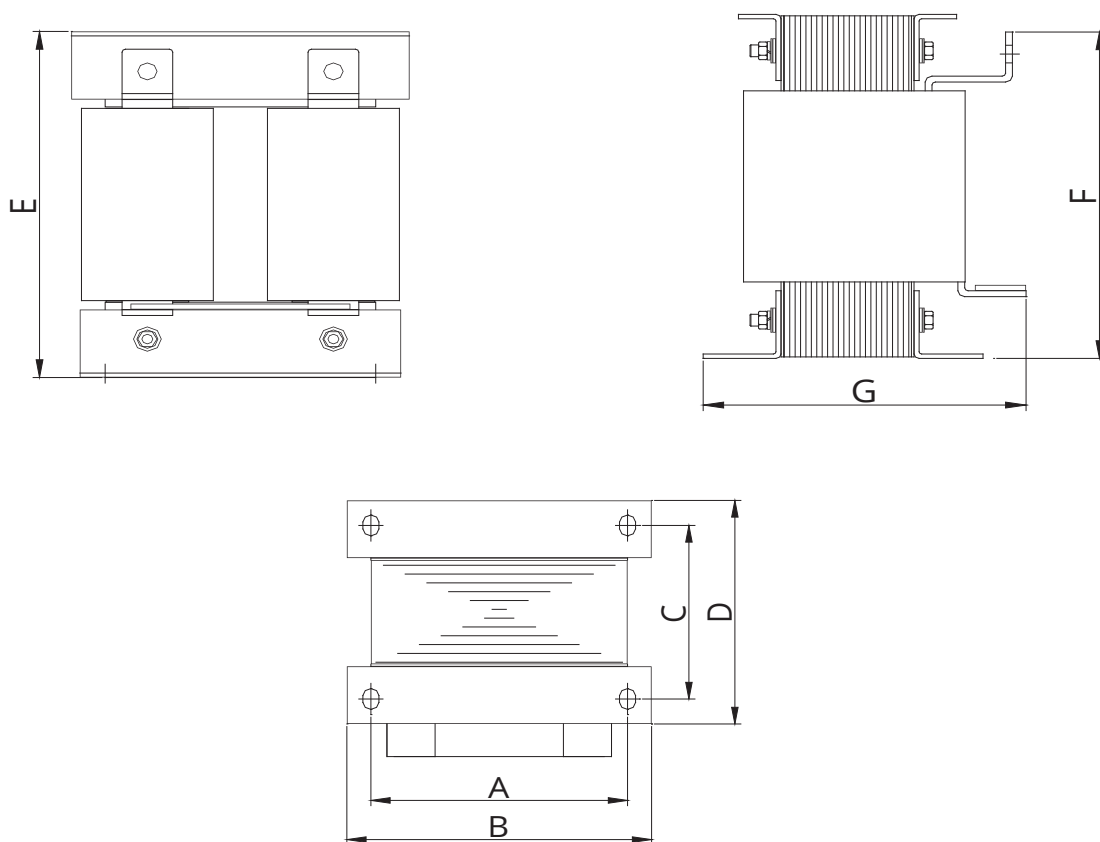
Внешний вид и размеры реактора постоянного тока
